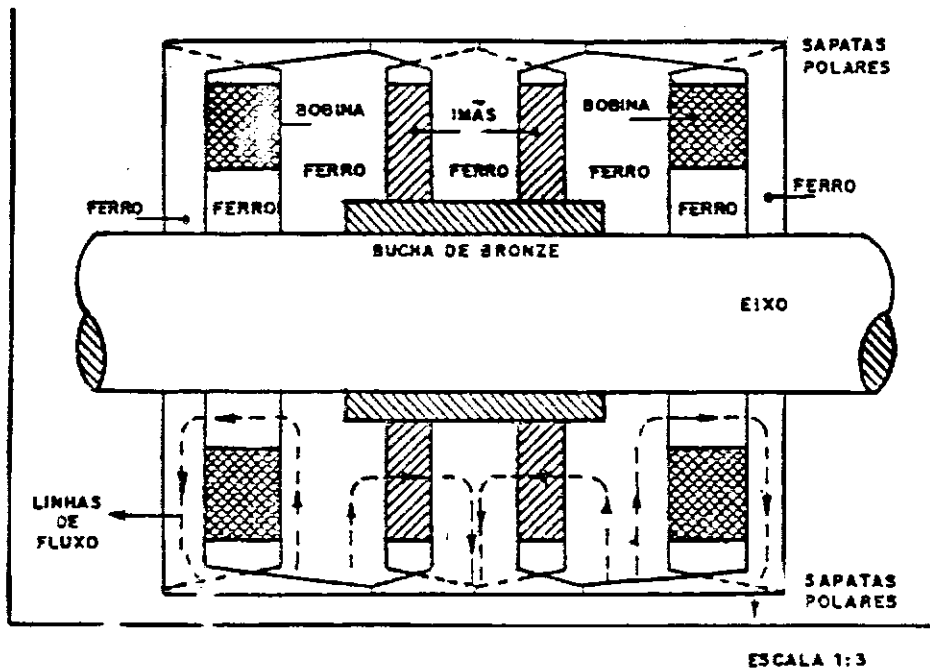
Corte Axial do Rotor do Alternador do SCEE Elektro.
